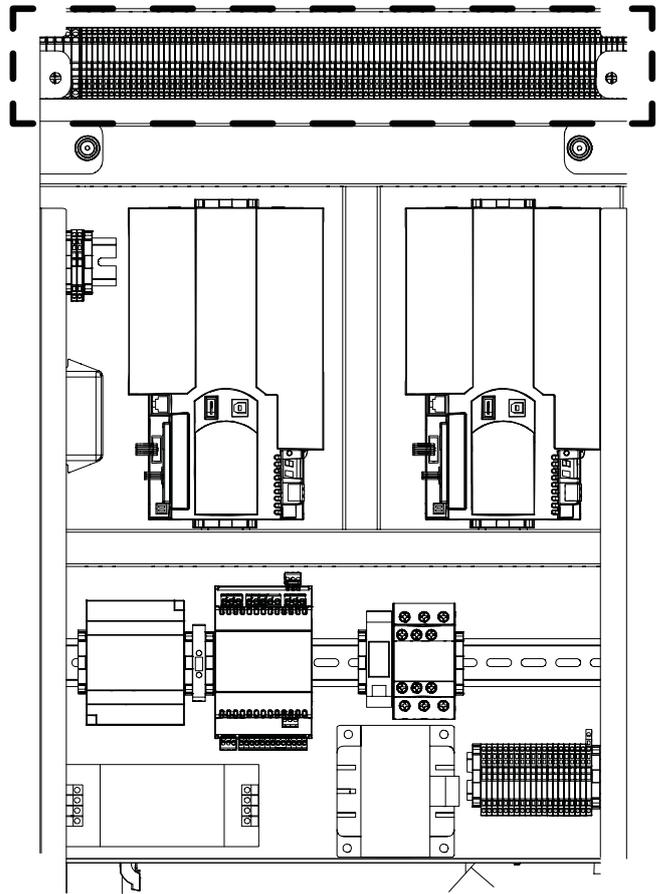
Kabeldurchführungen an Rückseite der Wärmepumpe
